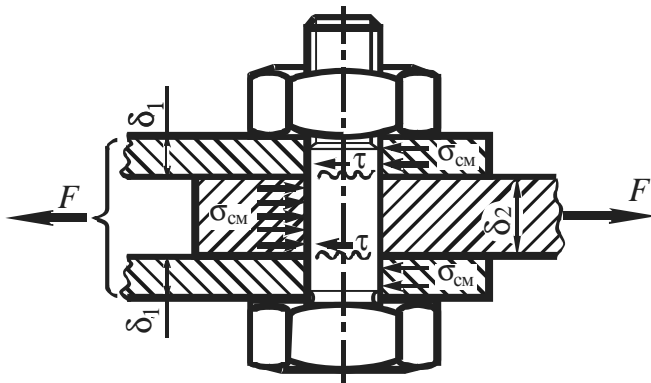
Схема болта установленного в отверстие деталей без зазора
